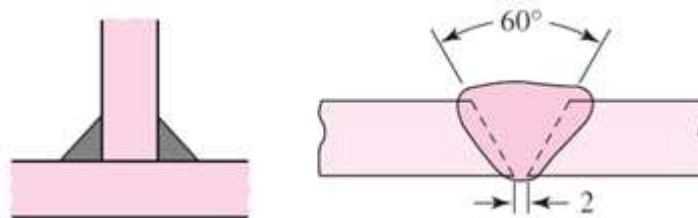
Esquema de soldadura tipo filete (izquierda) y tipo ranura (derecha)
